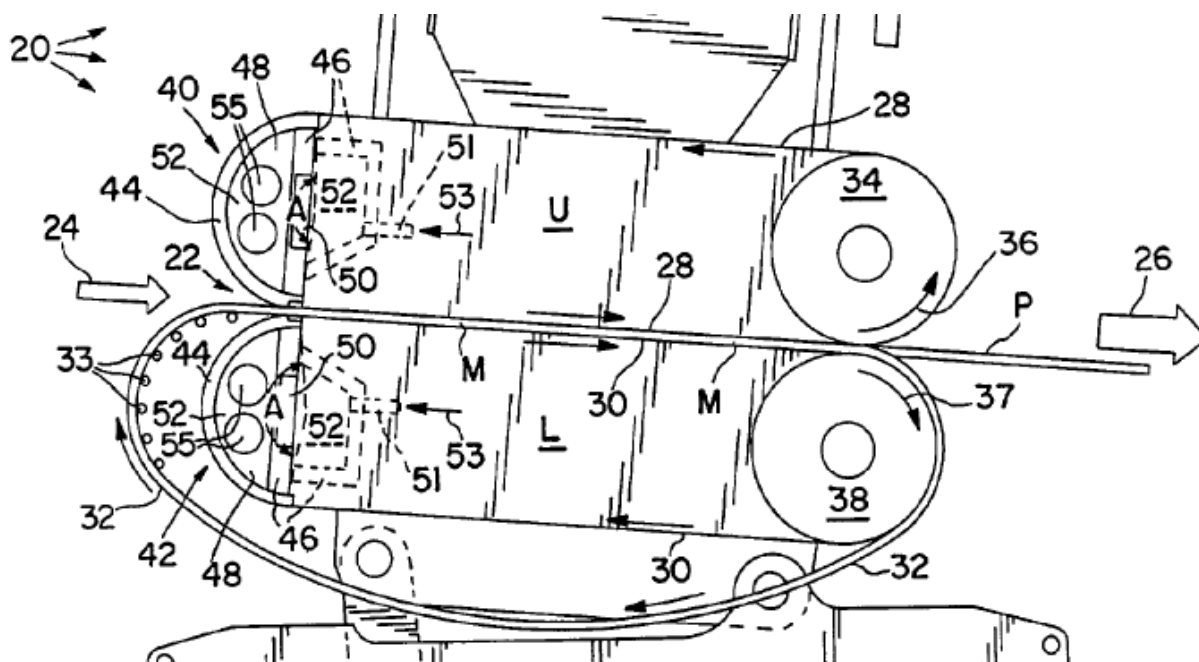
15. Схема усовершенствования двухленточной литейной машины Хазелетт по патенту Германии № DE60033667 американской компанией HAZELETT STRIP CASTING CORP (обозначения в тексте)
